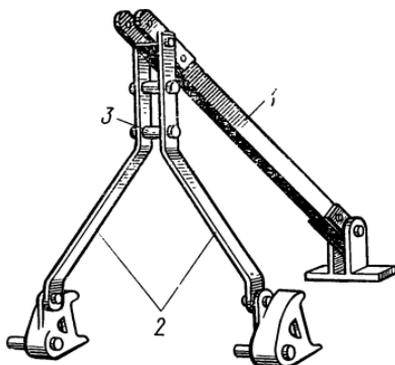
Универсальная навеска (вариант сборки для агрегатирования с тракторами ДТ-54А, Т-74, ДТ-75):
